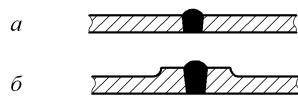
Типы сварного соединения стенок бака: а – без утолщения; б – с утолщением
